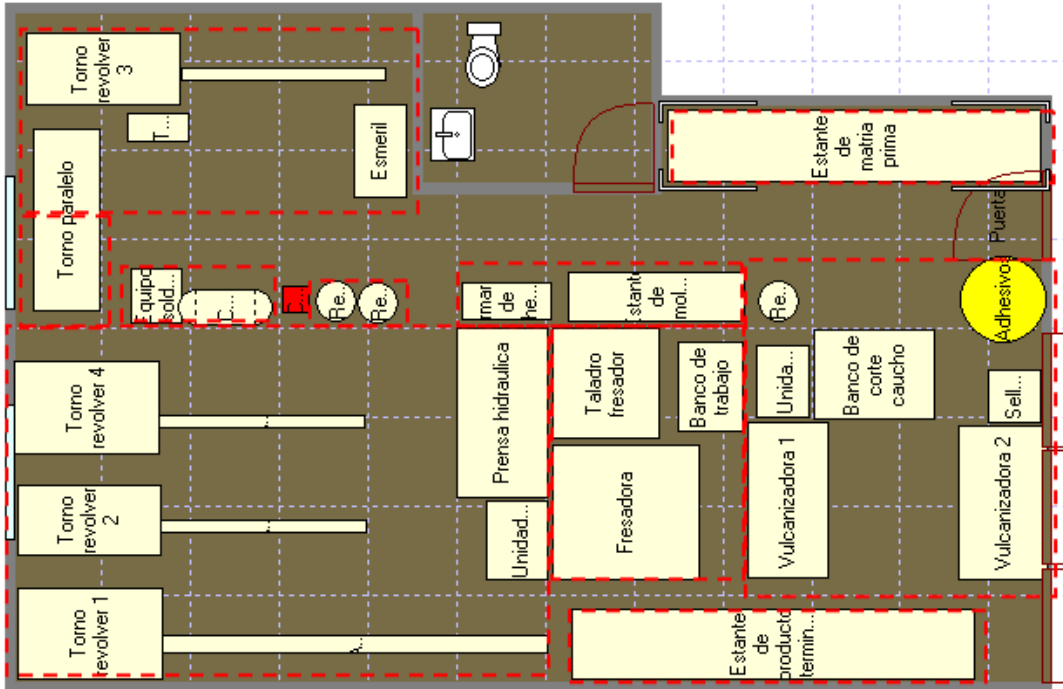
Propuesta A de Layout de planta de manufactura de autopartes. Fuente: Propia
